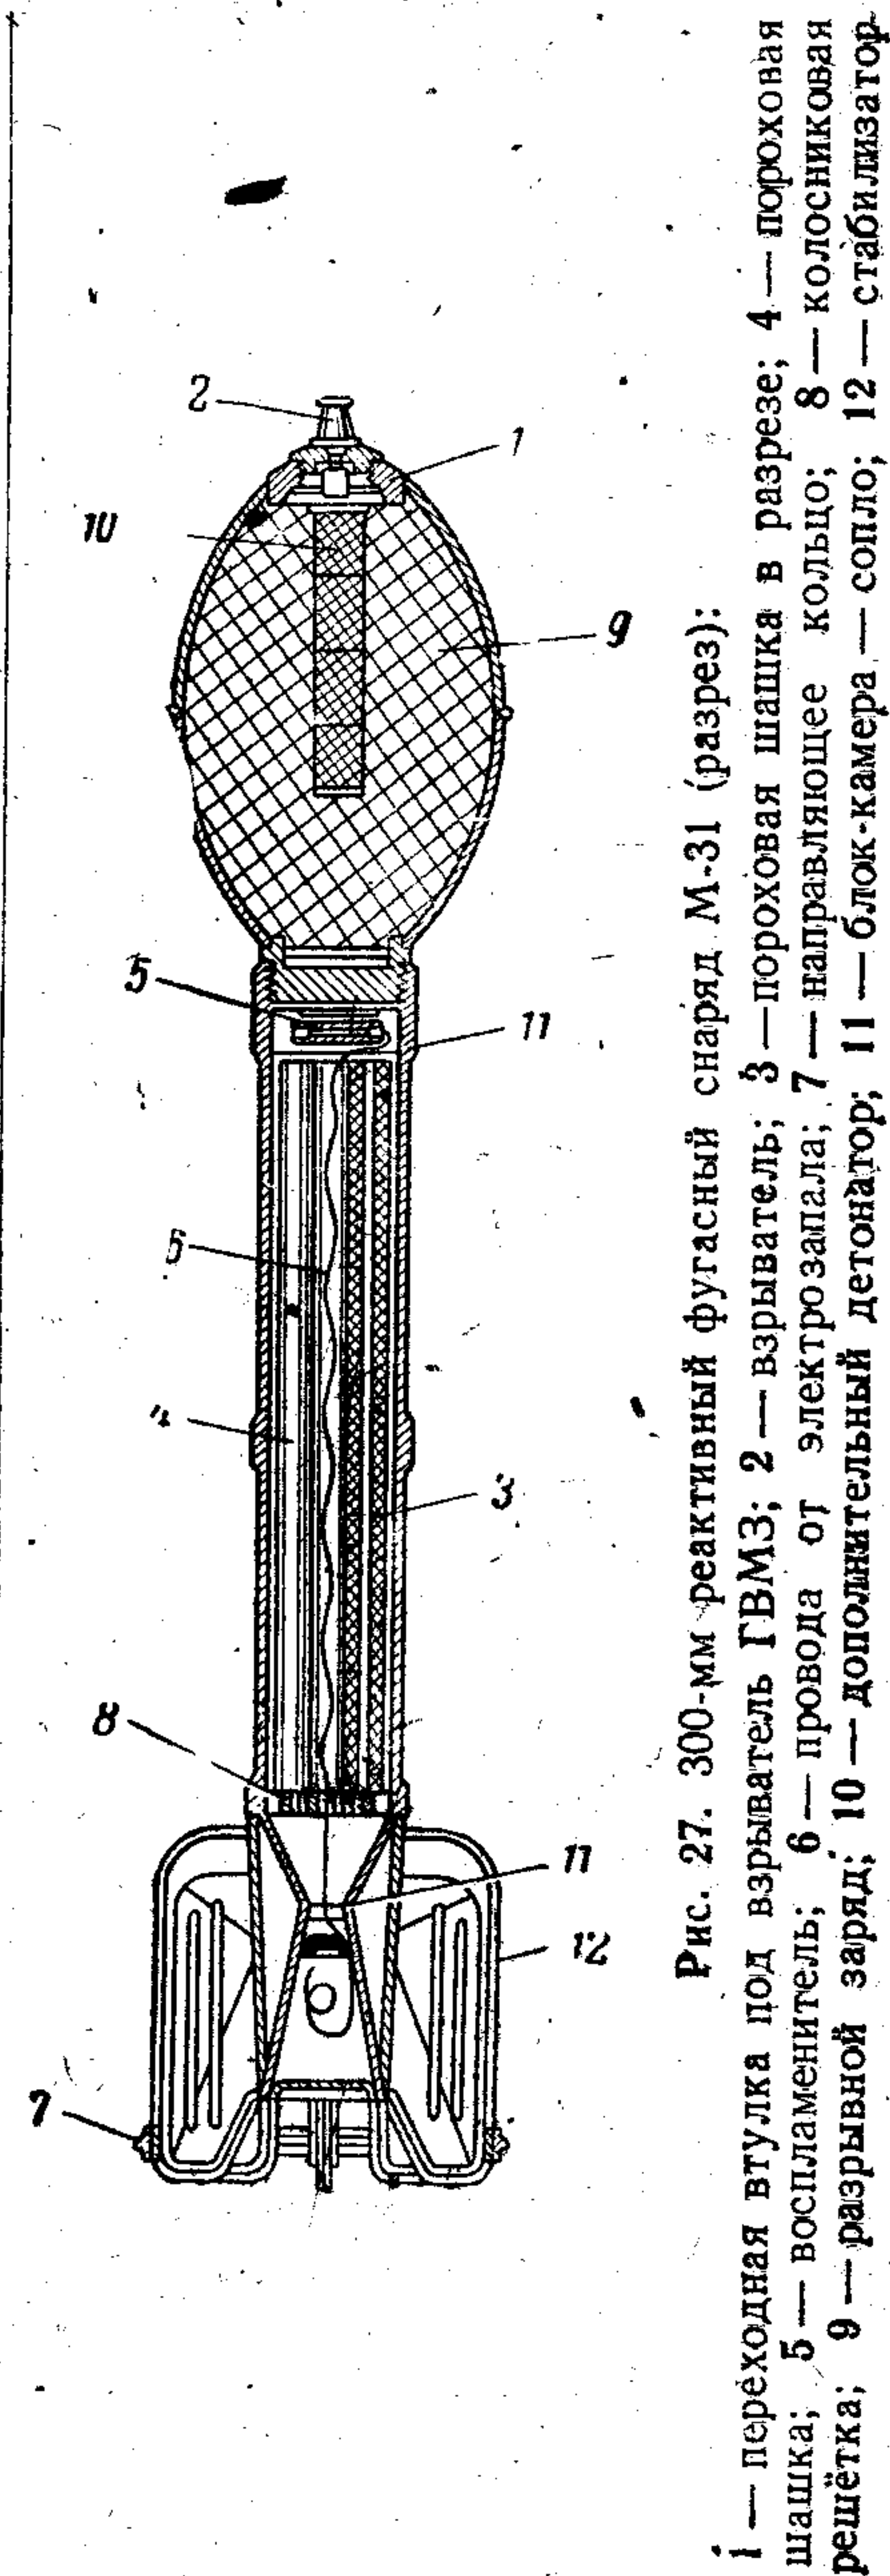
300-мм реактивный фугасный снаряд М-31 (разрез):
